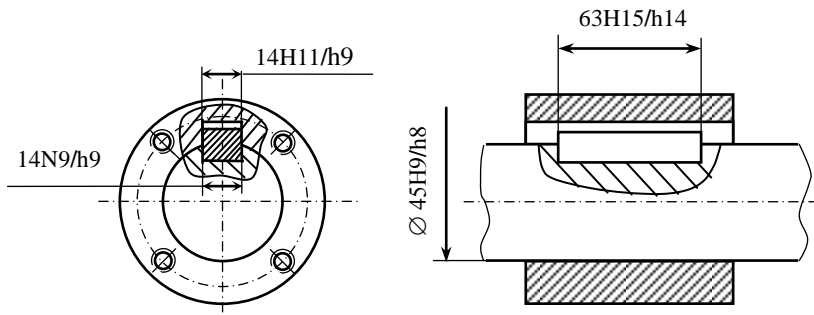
Пример обозначения на сборочном чертеже (общем виде) размеров и допусков шпоночного соединения и соединения вала со ступицей
